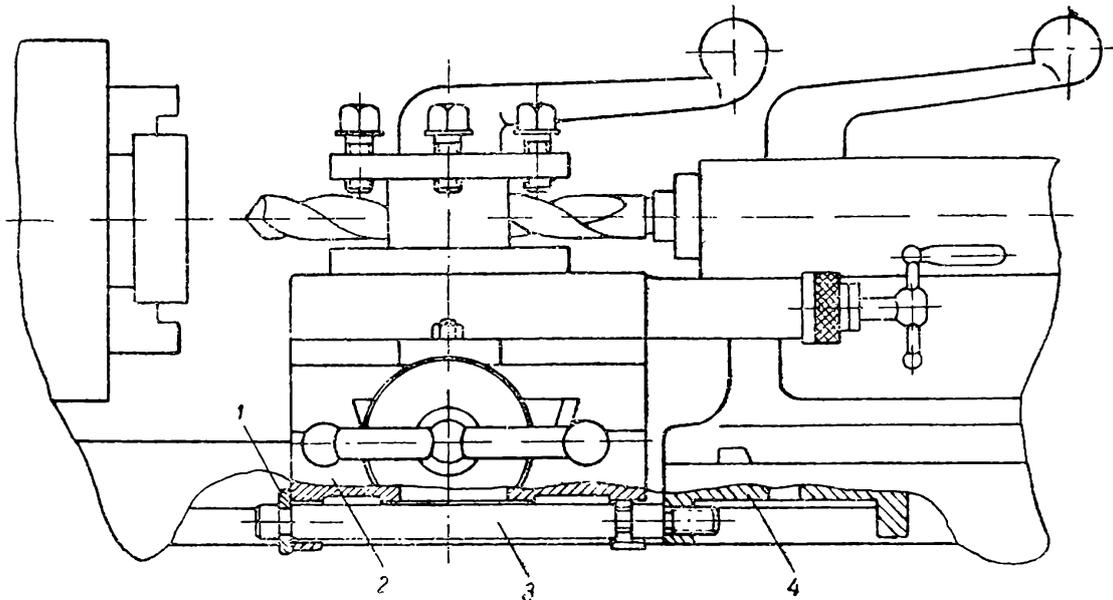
Устройство для механического перемещения задней бабки токарного станка при сверлении:
